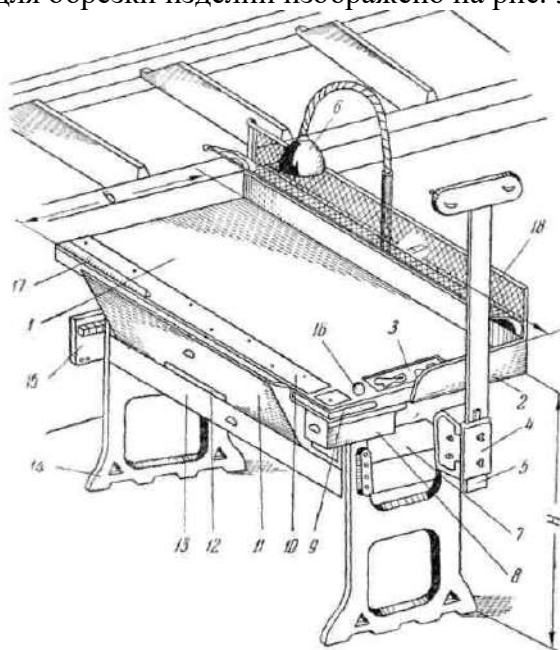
Типовое рабочее место для обрезки изделий: 1 — стол; 2 — борт стола высотой 120 мм; 3 — углубление для ножниц; 4 — направляющая стойка; 5 — кронштейн для лекал; 6 — светильник; 7 — ящик для личных вещей; 8 — ящик для мела; 9 — выдвижная рамка для
